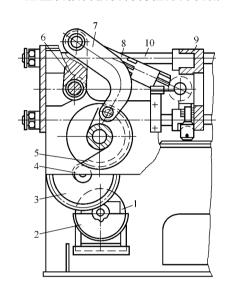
全机械式合模机构 1—电动机; 2—减速箱; 3,4—齿轮; 5—扇形齿轮; 6—曲肘; 7—构件; 8—连杆; 9—动模板; 10—拉杆
